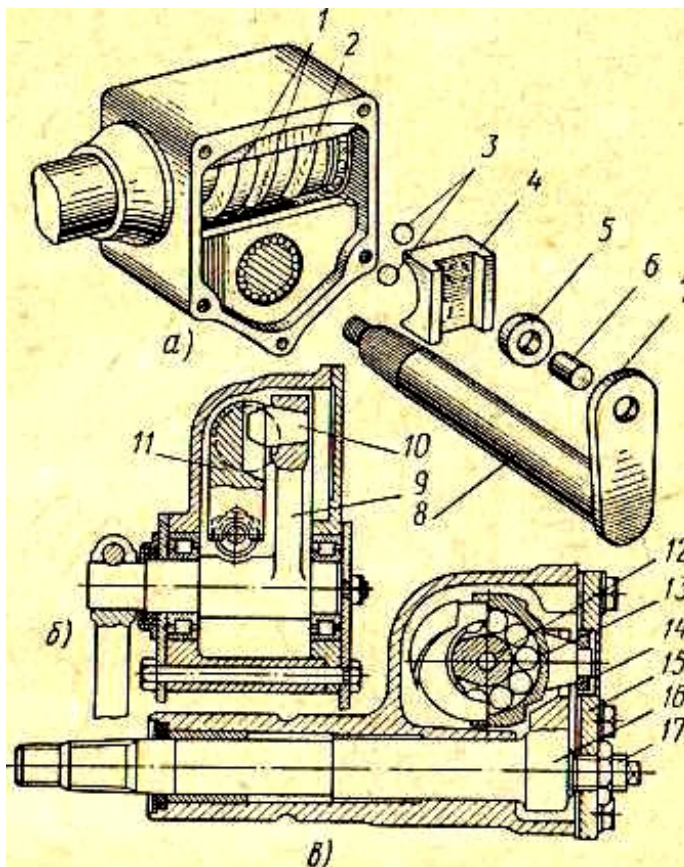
Рулевые механизмы с винтовой передачей и кривошипом или рычагом
